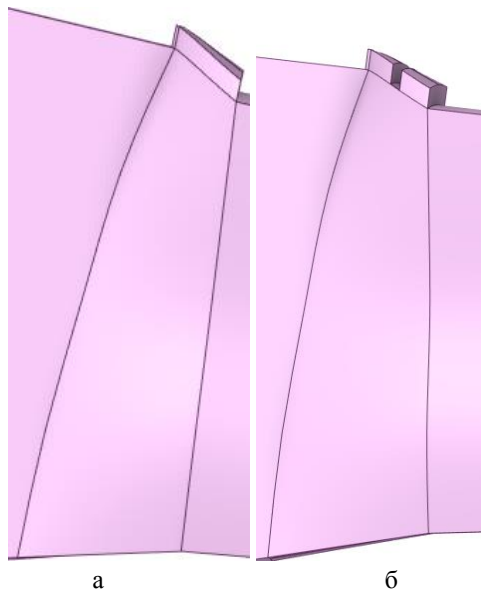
Модель робочого колеса вентилятора з надроторним пристроєм:
